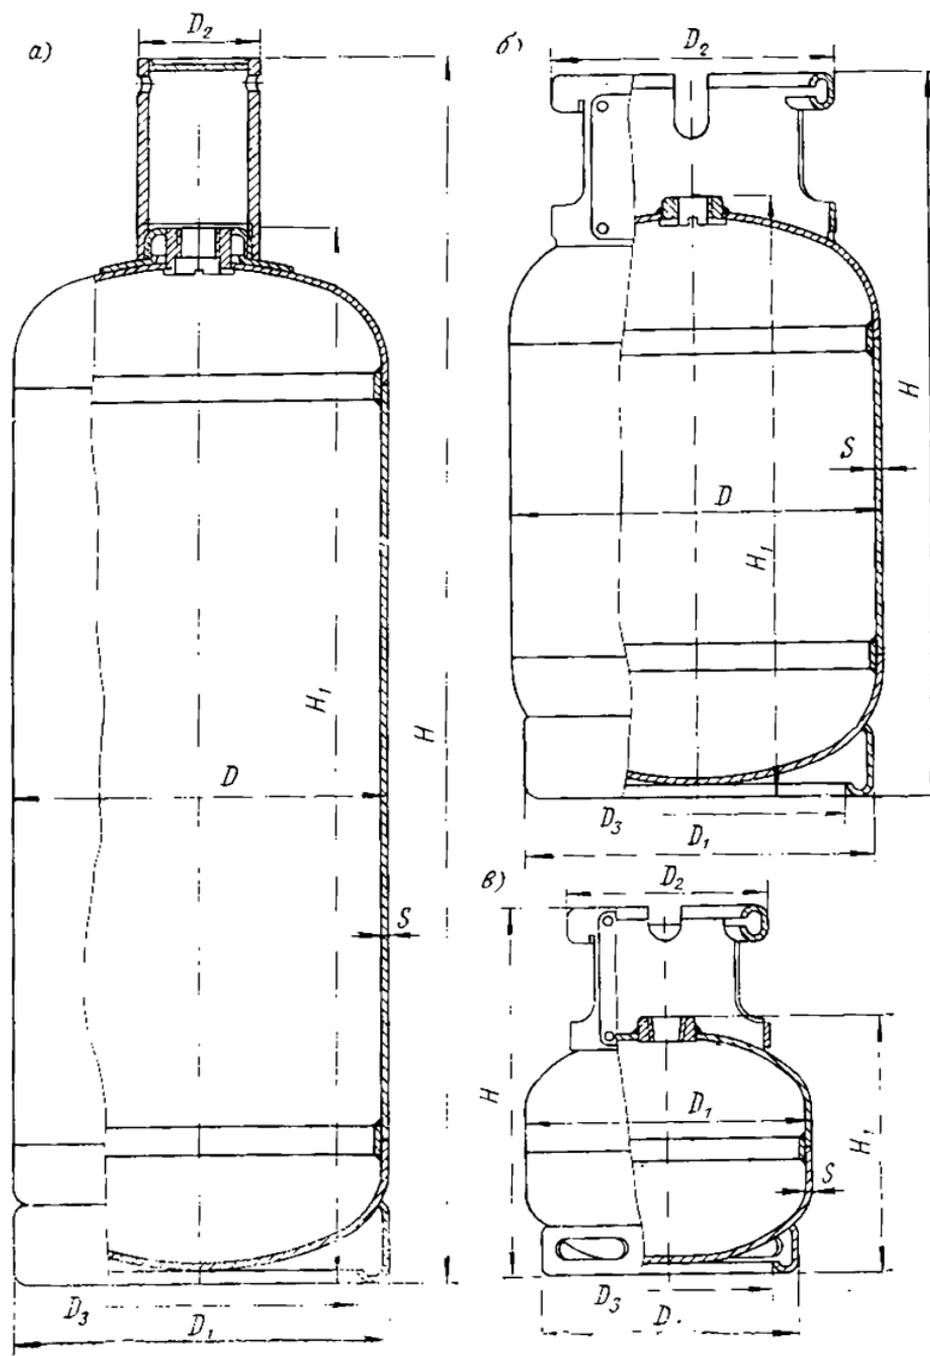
Стальные сварные баллоны для сжиженных газов
